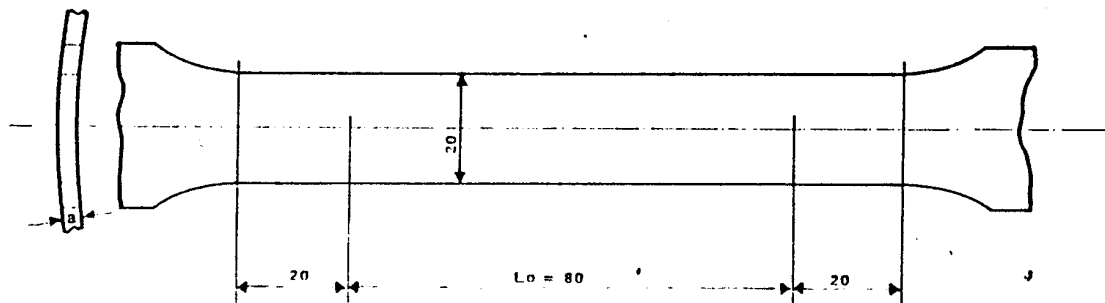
C. Probeta para ensayo de tracción de soldadura
